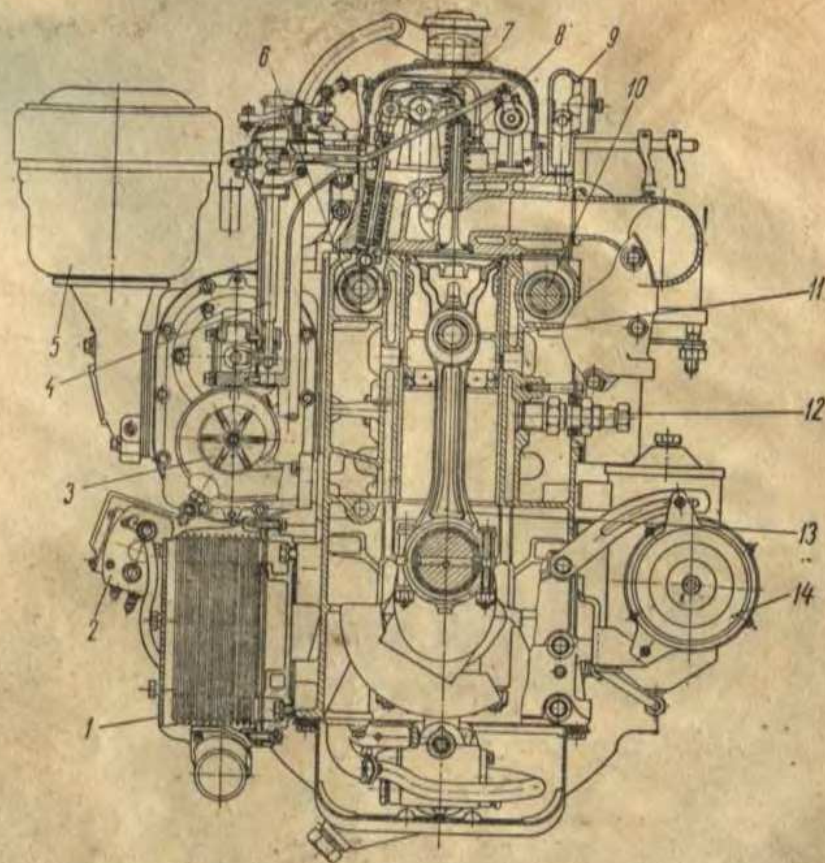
Поперечный разрез двигателя ЯАЗ-М206А:
